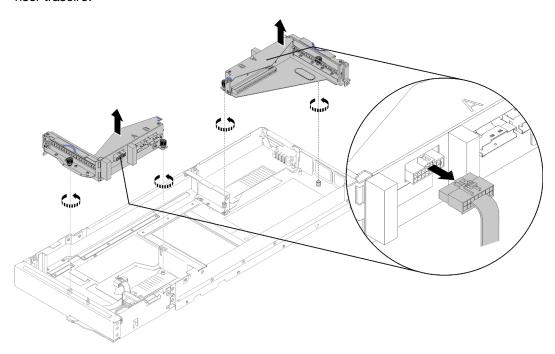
Desconectando o cabo diverso da placa riser frontal e removendo os compartimentos da placa riser do nó de expansão
